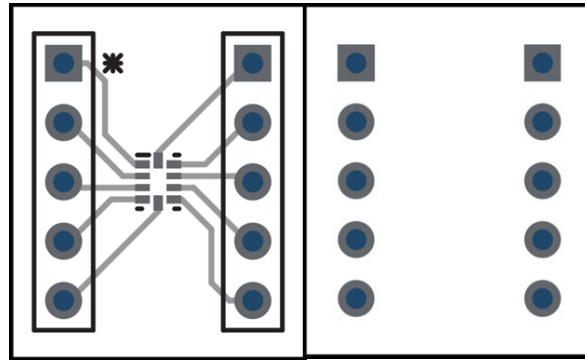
RUG 封装顶层 (左) 和底层 (右) 的 PCB 布局
